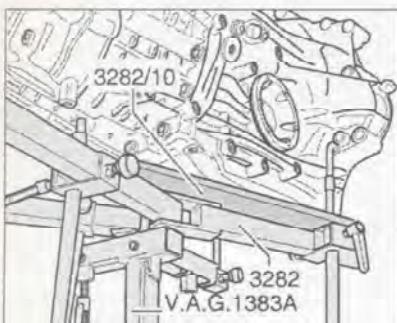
Закрепите приспособление для крепления коробки передач 3282 с выверочной доской 3282/10 на подъемнике и установите последний под коробку передач.
